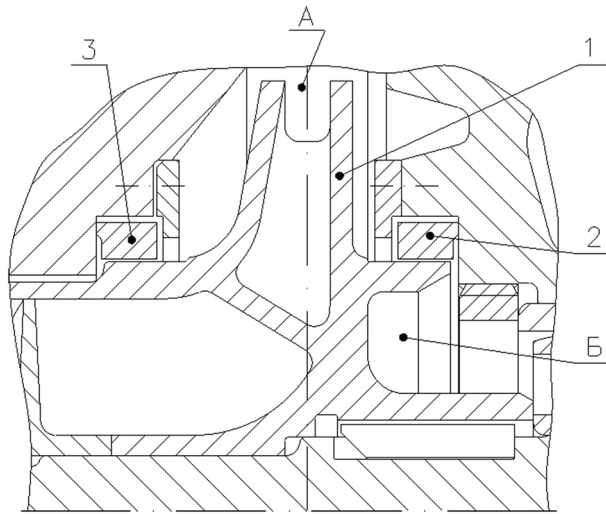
Конструкция уплотнений центробежного колеса с помощью плавающих колец:
